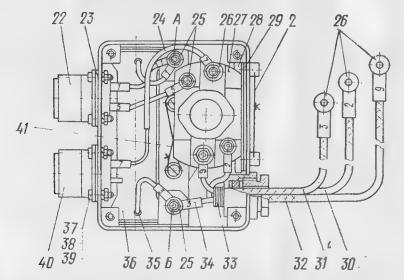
Соединительный блок 2А26.Сб 10-53:
